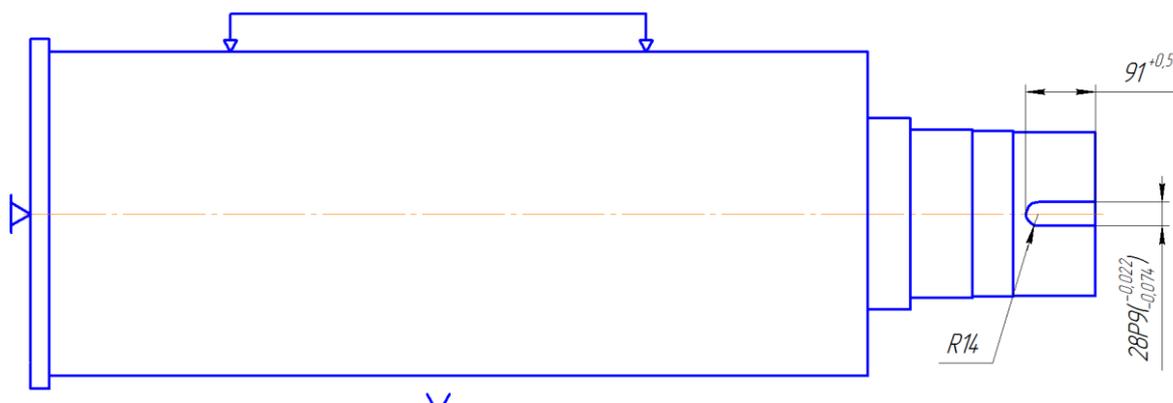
Эскиз базирования заготовки на 010 горизонтально-расточной операции.
